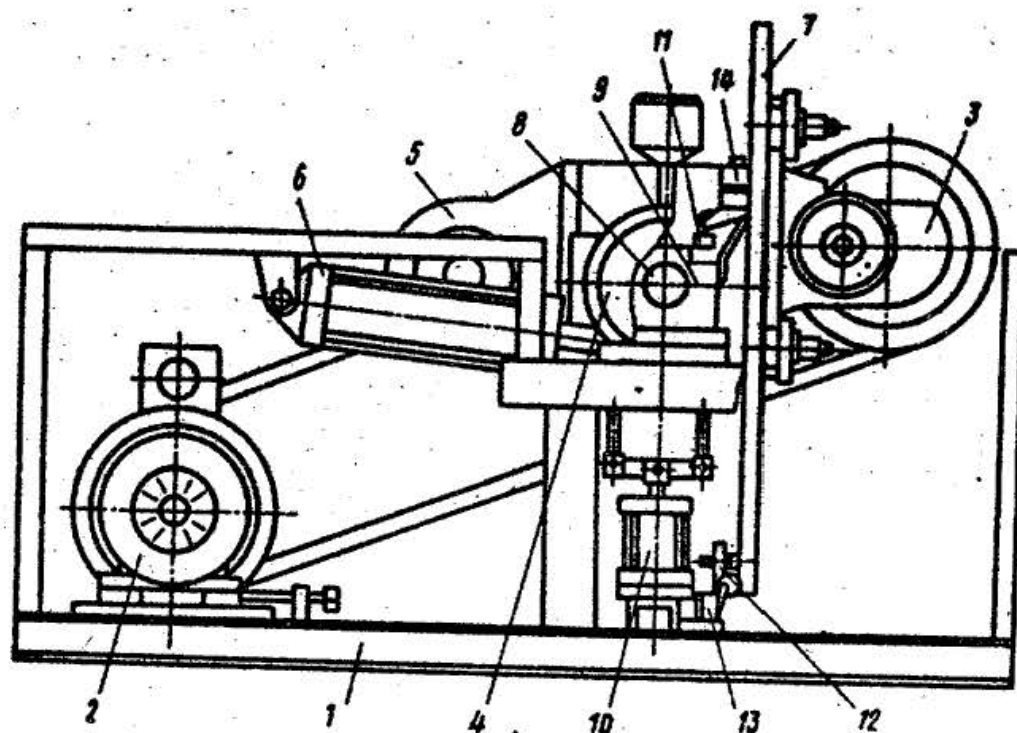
Стенд для испытания и обкатки коробок передач
